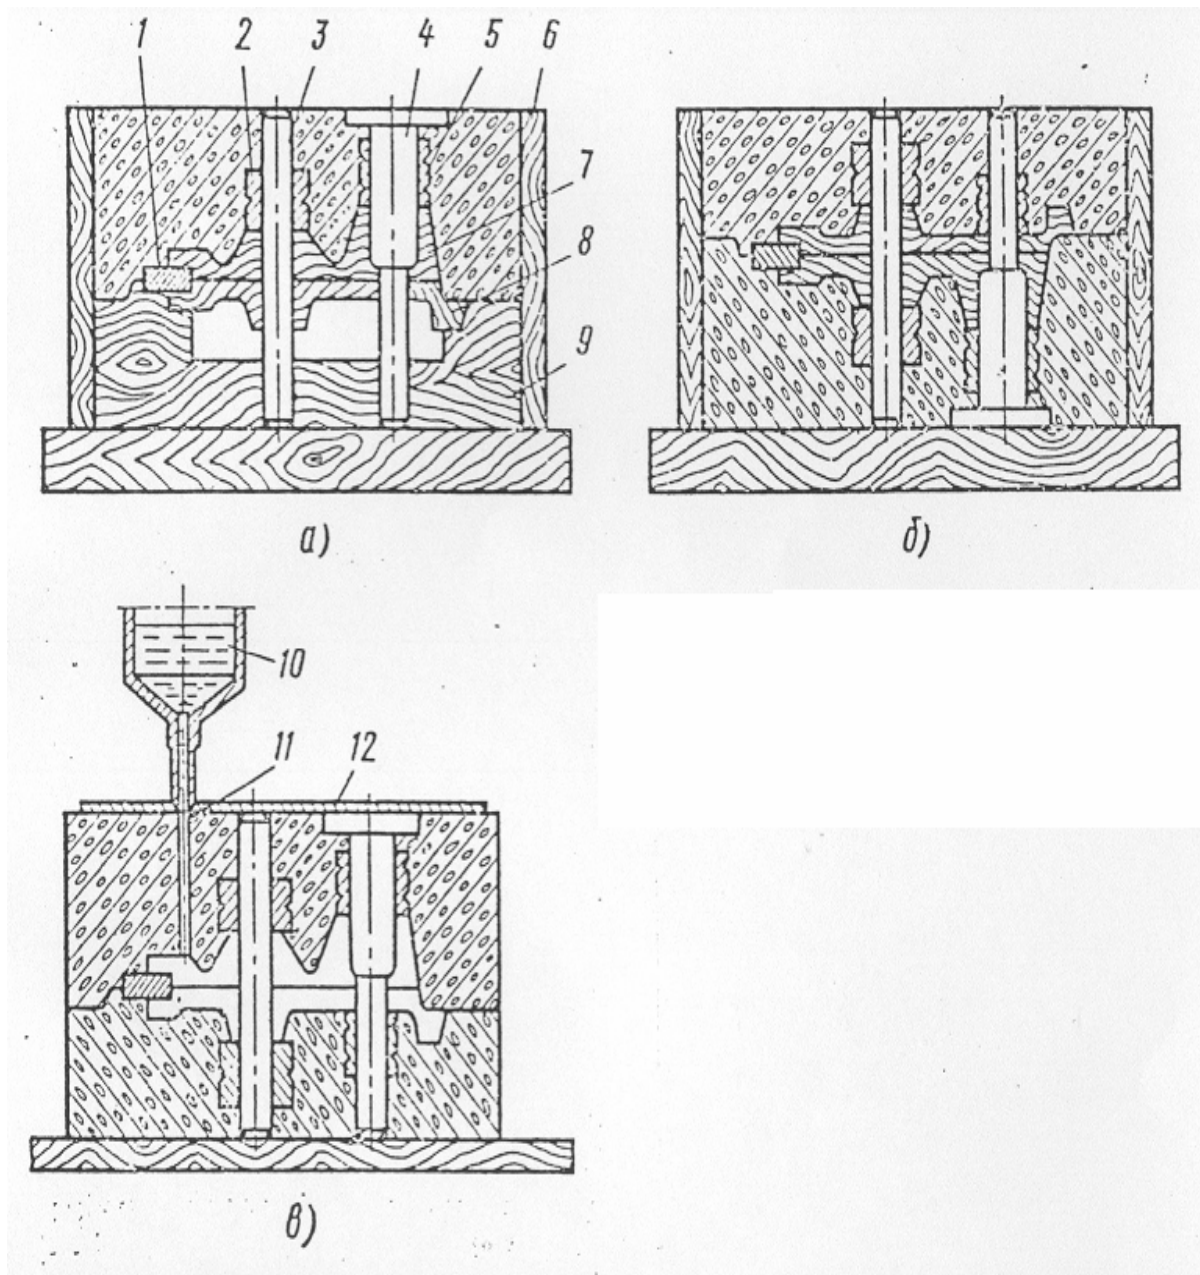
Схема изготовления гипсовой пресс-формы: а, б – изготовление верхней (а) и нижней (б) полуформ; в – запрессовка модельного состава; 1 – вкладыш; 2,5 – втулки; 3,4 – стержни; 6 – рамка; 7,8 – половины моделей; 9 – модельная плита; 10 – модельный состав; 11 – литниковый канал; 12 – плита.
